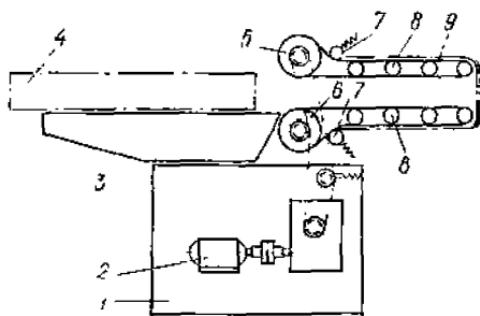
Схема станка для надевания чехла на двусторонний матрац
